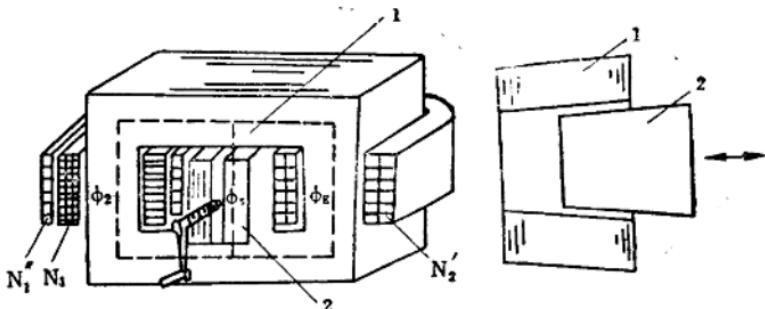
6 动铁式交流弧焊变压器电磁结构原理图
